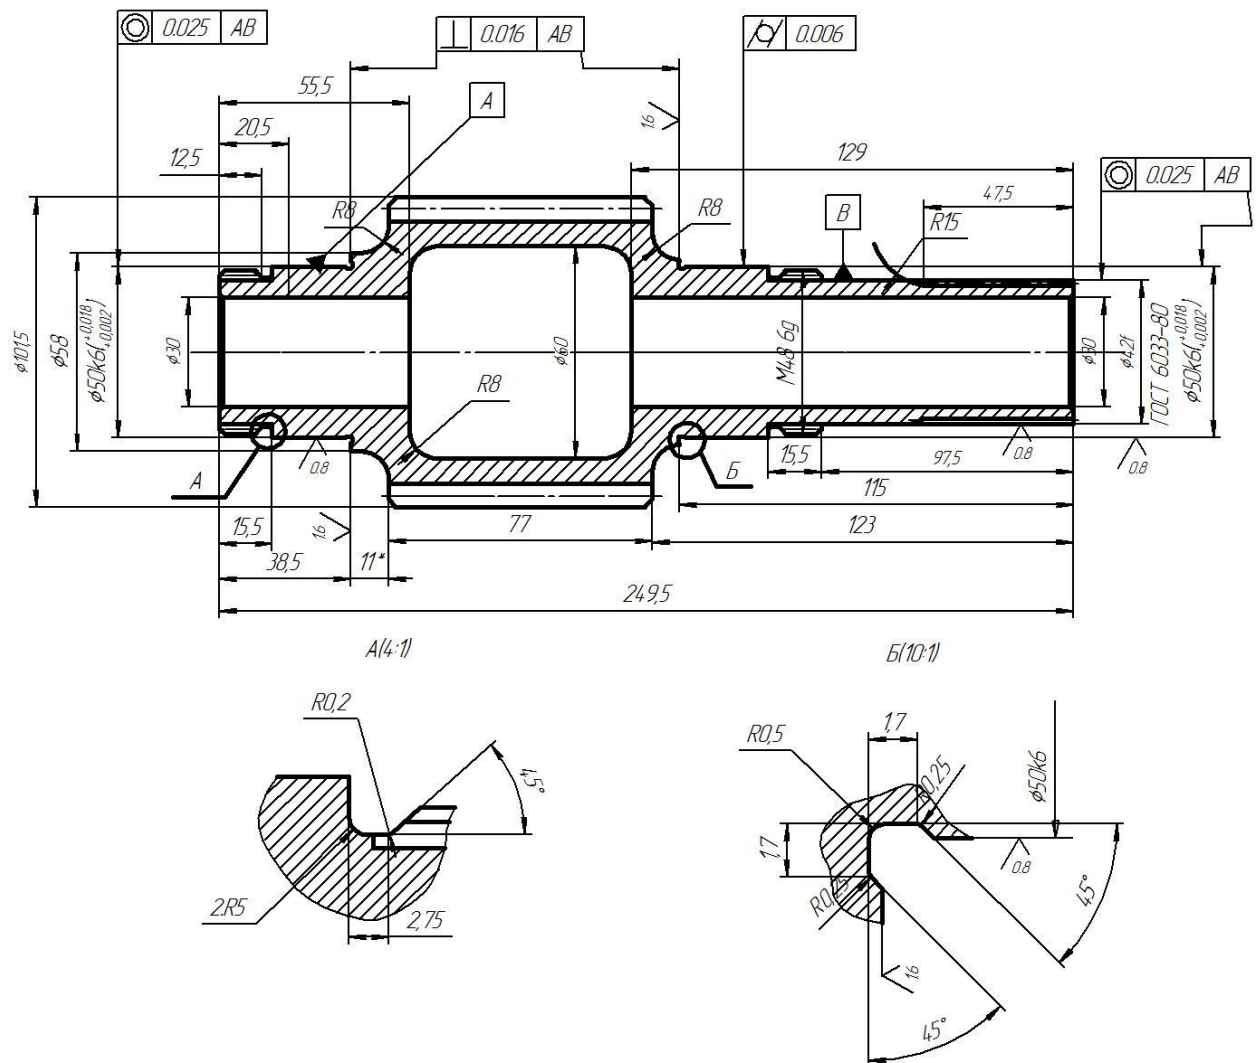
Вал-шестерня главного редуктора вертолета
